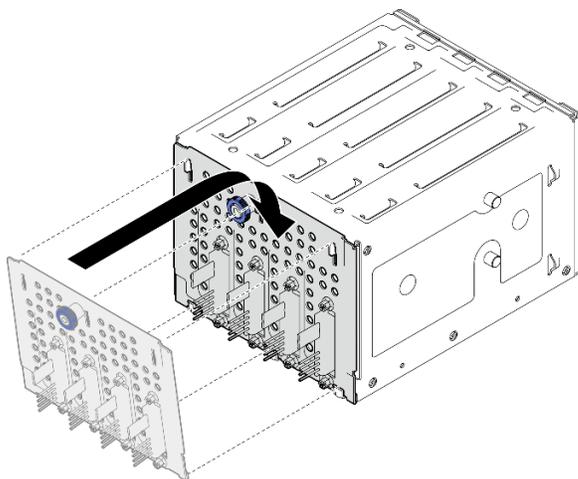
Installation de la plaque arrière d'unité à remplacement standard
